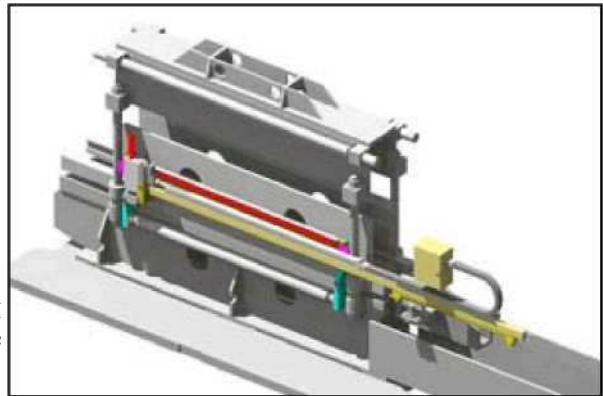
Преобразователь и транспортер, показанные на стыковой сварочной машине TW®
